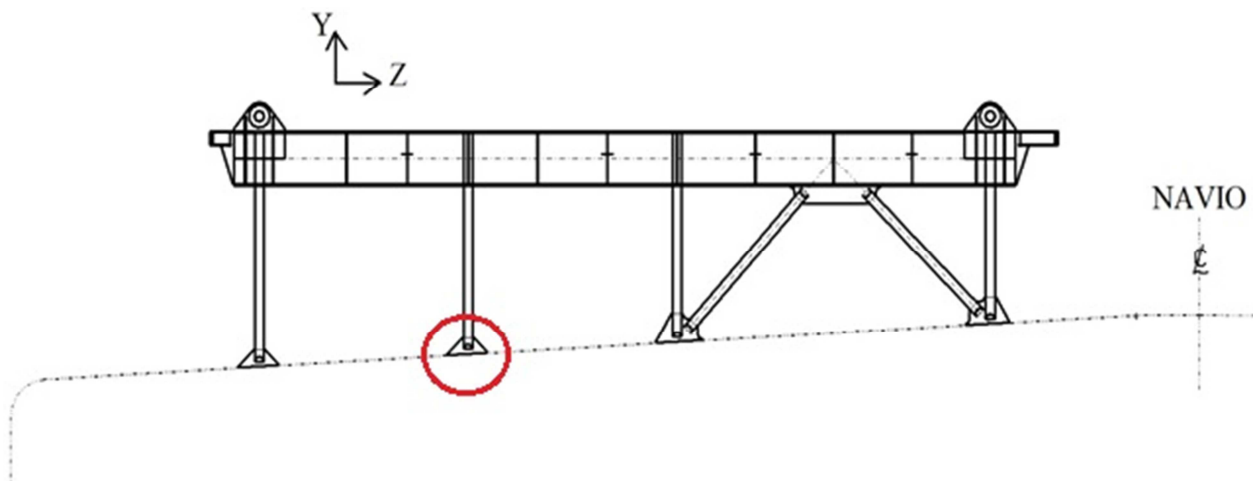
Seção transversal: diagonais típicas entre “frames”.
